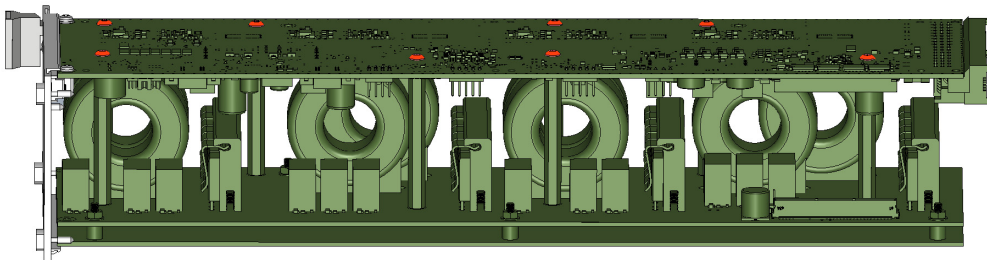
Lage des ES4455.2 Load Carrier Board (oben) mit Lastmodul (unten).
